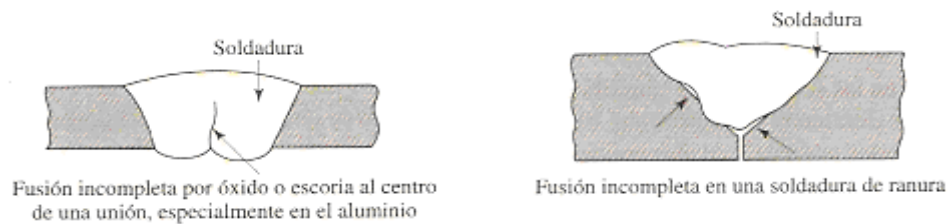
Cordones de soldadura de baja calidad, resultado de fusión incompleta
